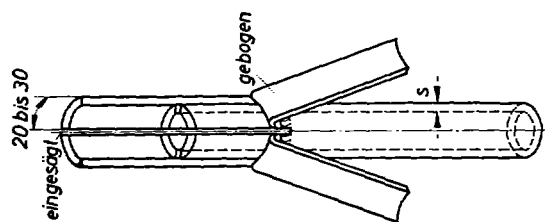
Rohr-Faltprobe für Rohrschweißer an $s = 1,5$ bis 2 mm (Prüfstück entsprechend Bild 9)
